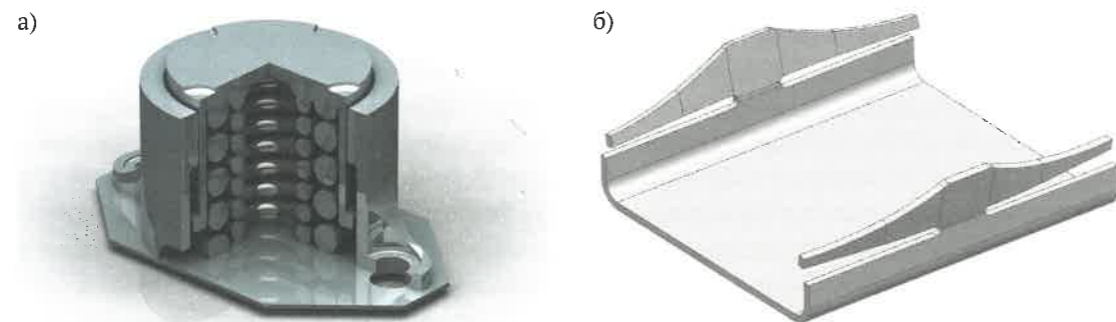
Совершенствование деталей тележки 18-9855, где: а) боковой скользуна цилиндрической формы; б) износостойкая скоба буксового проема
